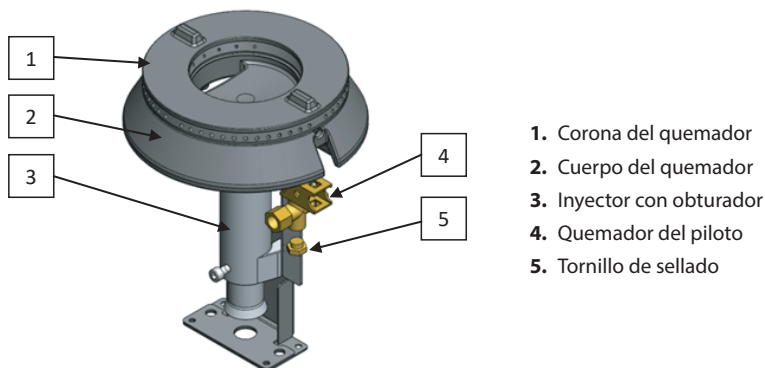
Diseño del quemador sobre el ejemplo de un quemador de 7 kW
